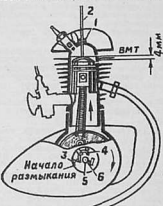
Схема установки зажигания: 1 — молоточек прерывателя, 2 — проволочка для определения верхней мертвой точки, 3 — неподвижный контакт прерывателя, 4 — подвижный прерывателя, 5 — кулачок, 6 — фетр для смазки кулачка.
